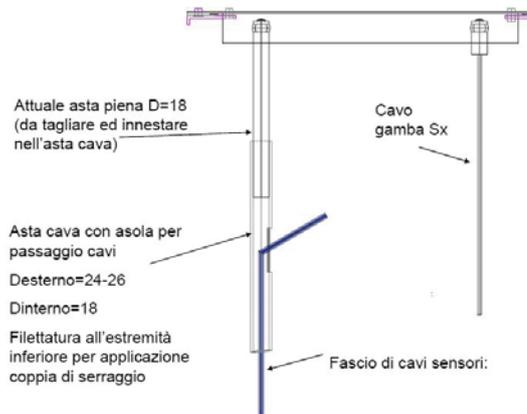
particolare dell'asta di sostegno modificata rispetto alla configurazione precedente.
